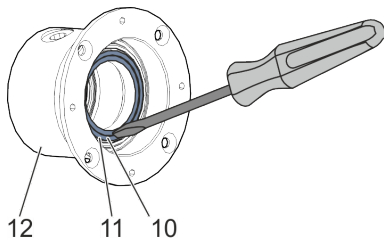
Démontage de la face de frottement de garniture mécanique
